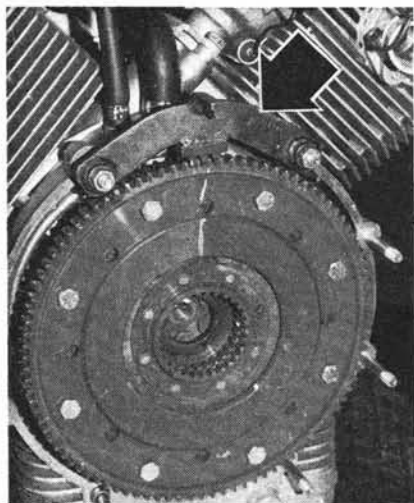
Outil pour bloquer la couronne (Photo RMT)
